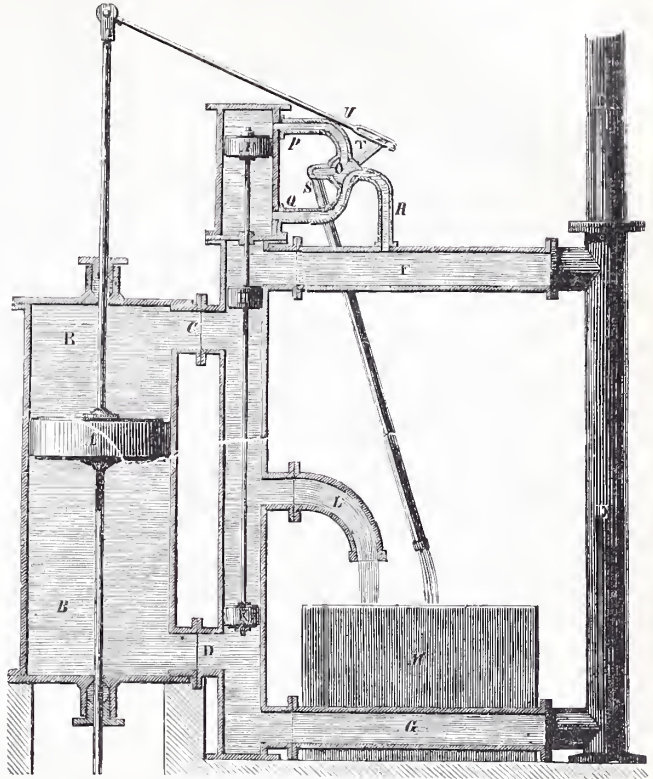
Doppelt wirkende Wasserfäulenmaschine.
